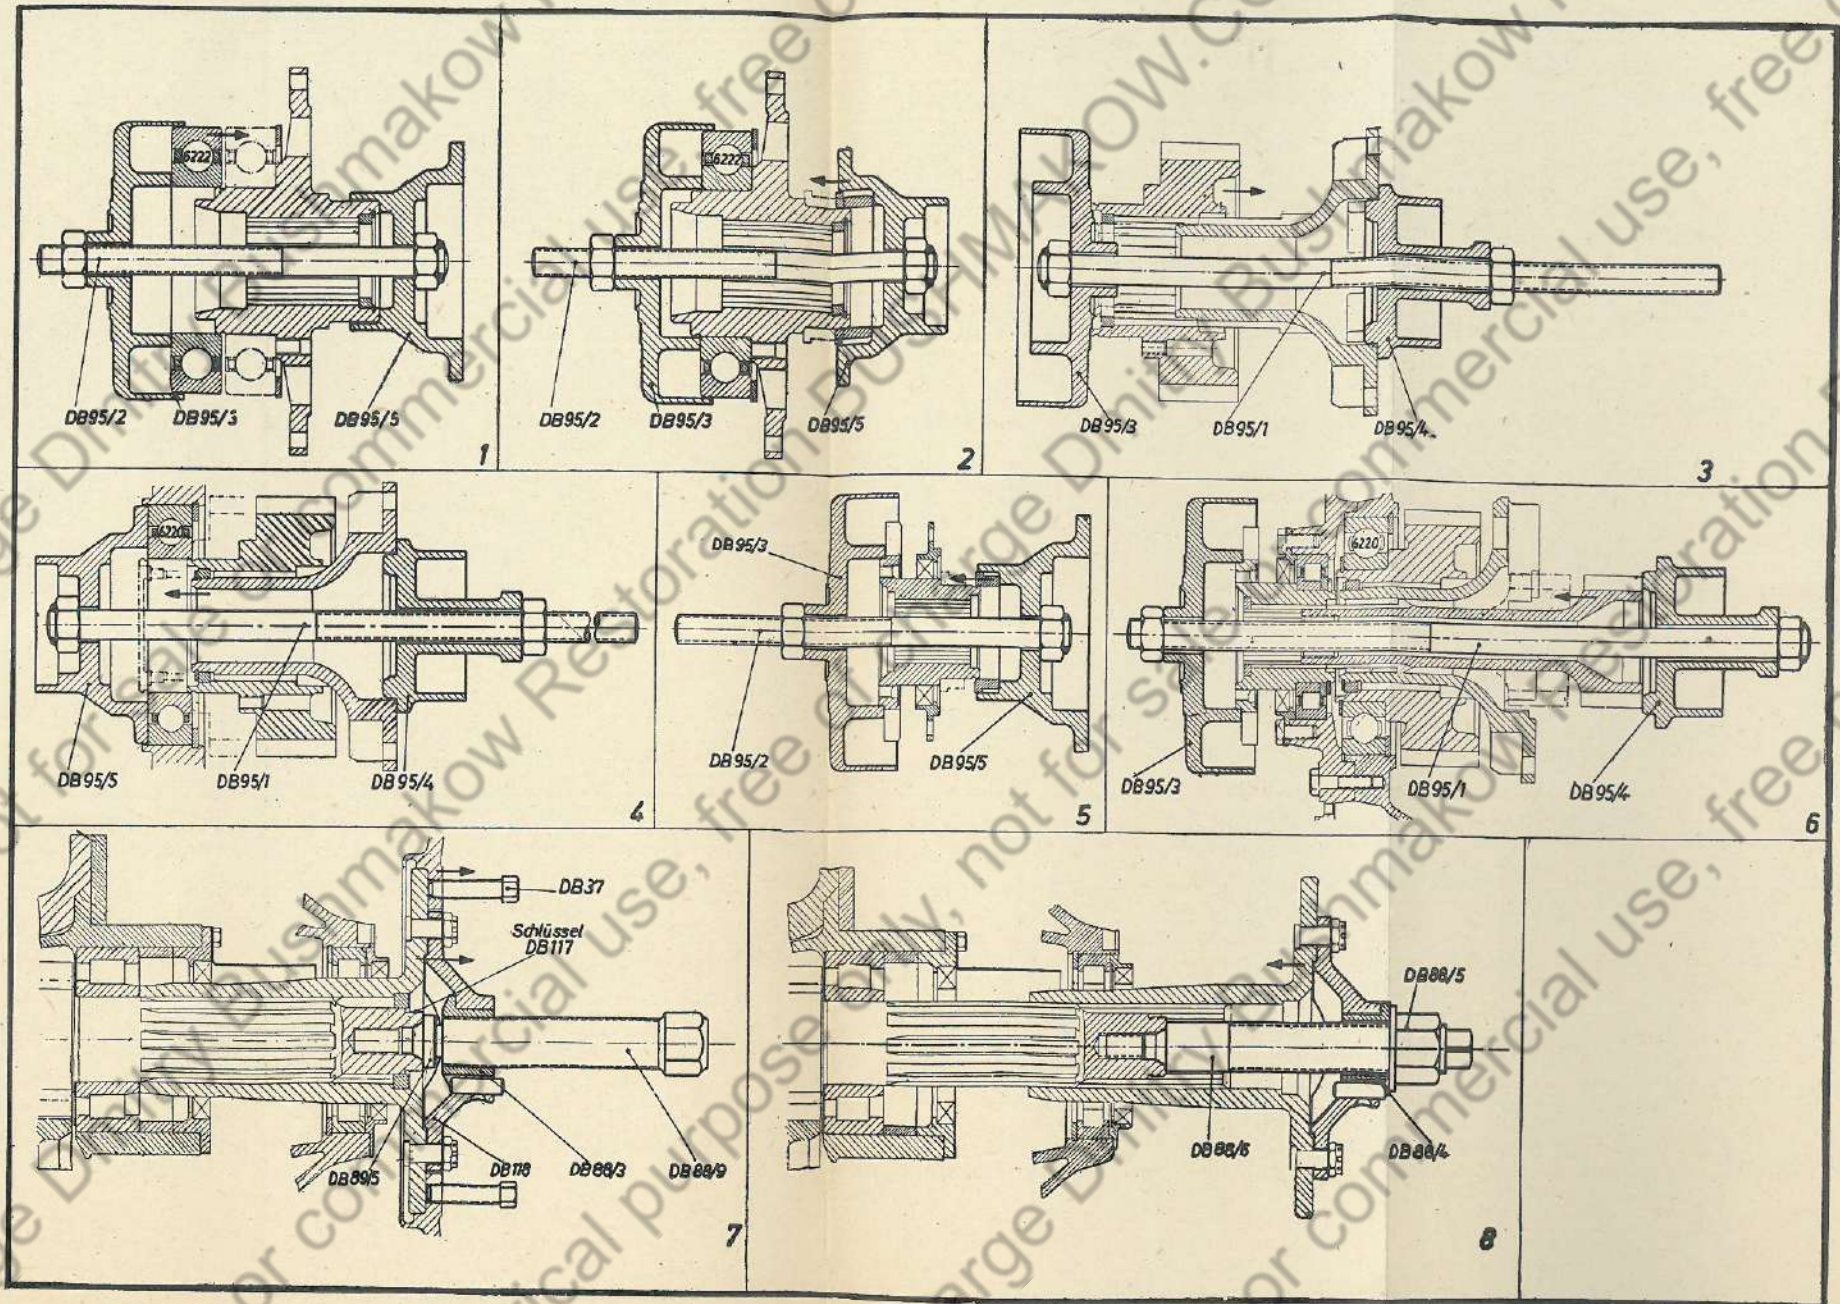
Lenkgetriebe, Einbau; Lenkbremse, Aus- und Einbau
